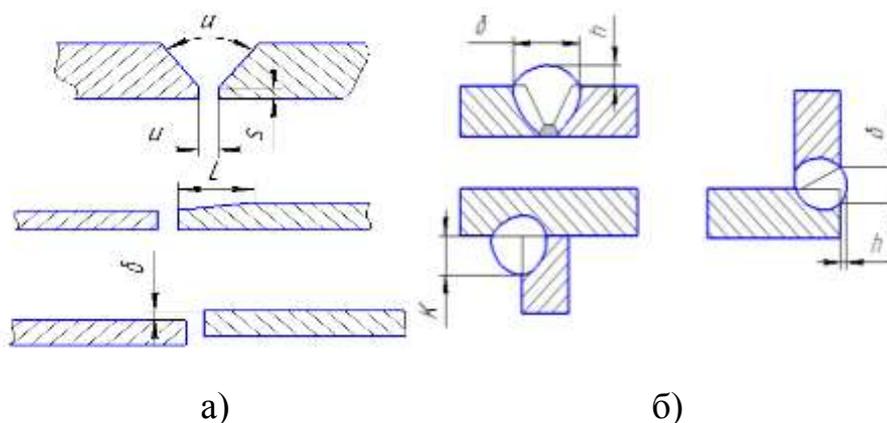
Элементы геометрической формы подготовки кромок под сварку (а) и шва (б): δ - ширина шва, h - высота шва, K - катет шва [20].
